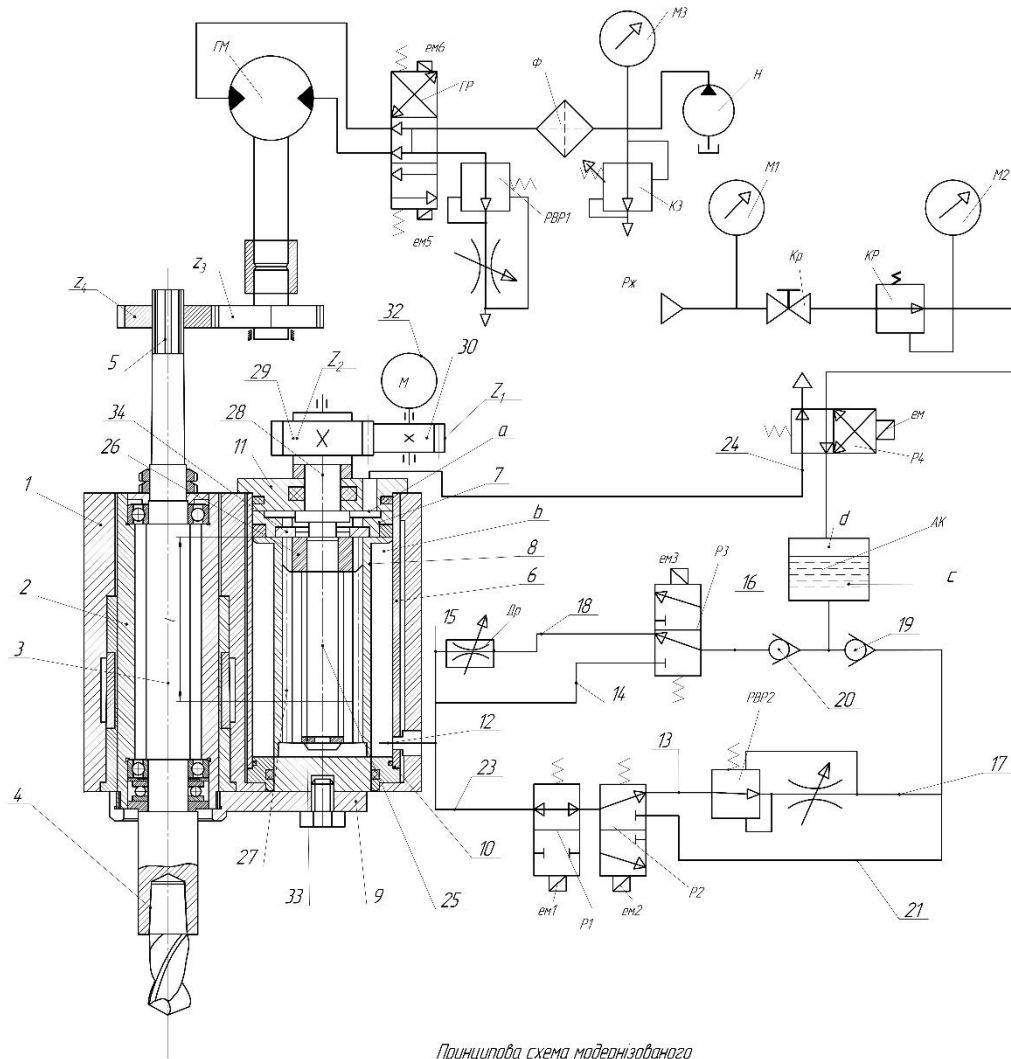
Принципова схема модернізованого вертикально-свердлильного верстата
